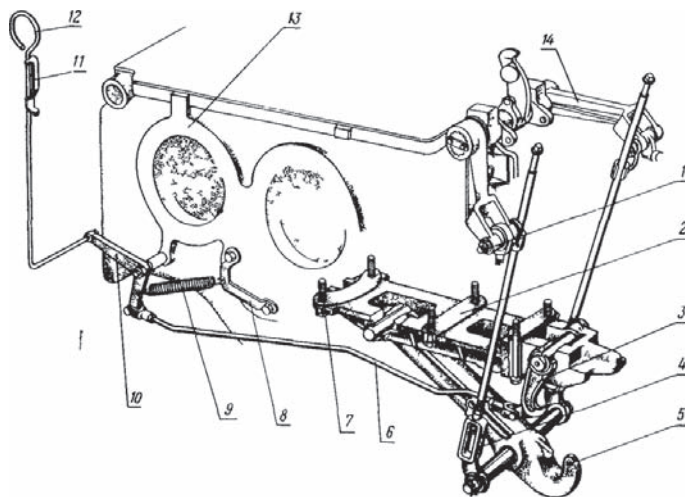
Гидрофицированный прицепной крюк. 1 — палец; 2 — кронштейн; 3 — захват; 4 — тяга; 5 — крюк; 6 — тяга; 7 — болт; 8 — кронштейн; 9 — пружина; 10 — рычаг; 11 — фиксатор; 12 — ру-
